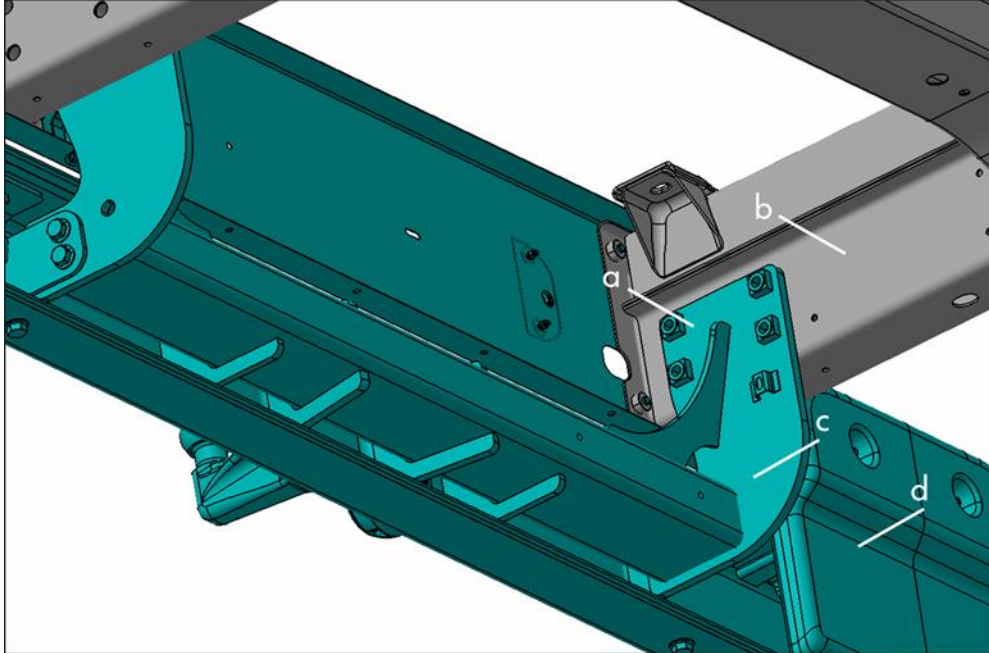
Montaje del enganche para remolque en el larguero del bastidor (vista desde la parte inferior derecha)
